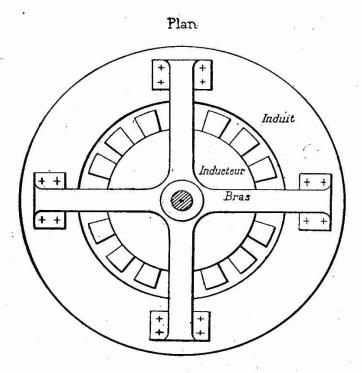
Alternateur à arbre vertical (type horizontal renversé). Vue en plan.
